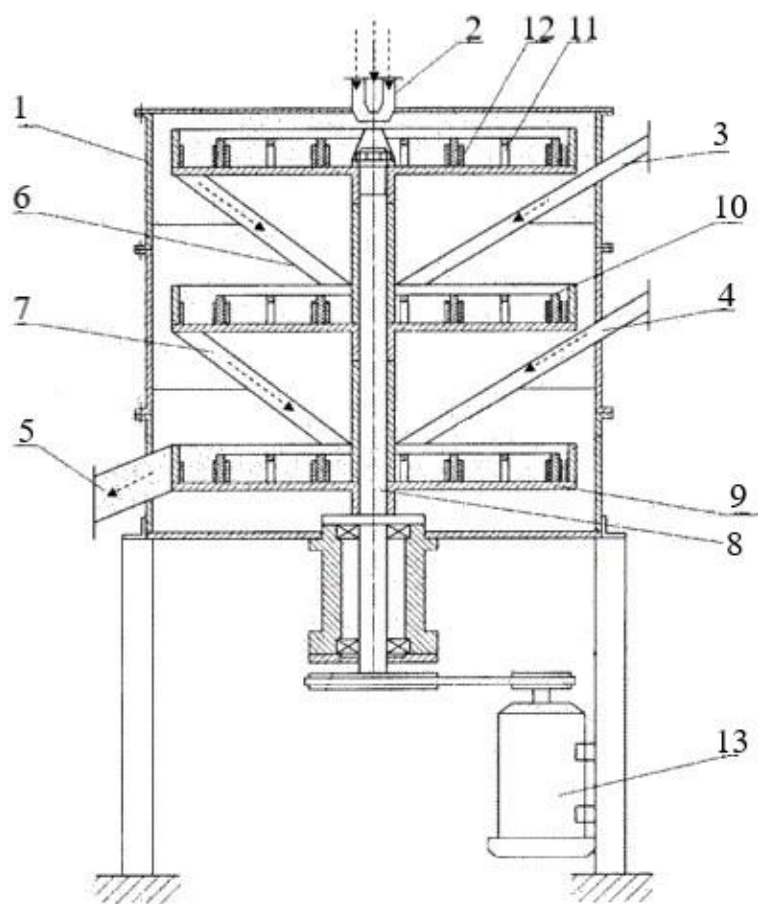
Схема центробежного смесителя (Пат. № 171699).
